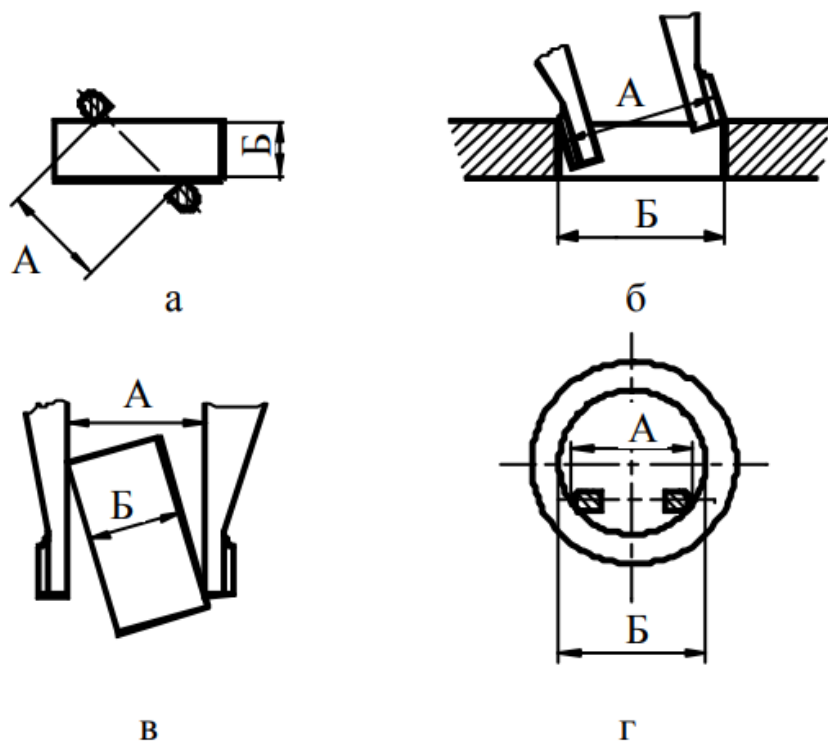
Приклади неправильної установки штангенциркуля:
